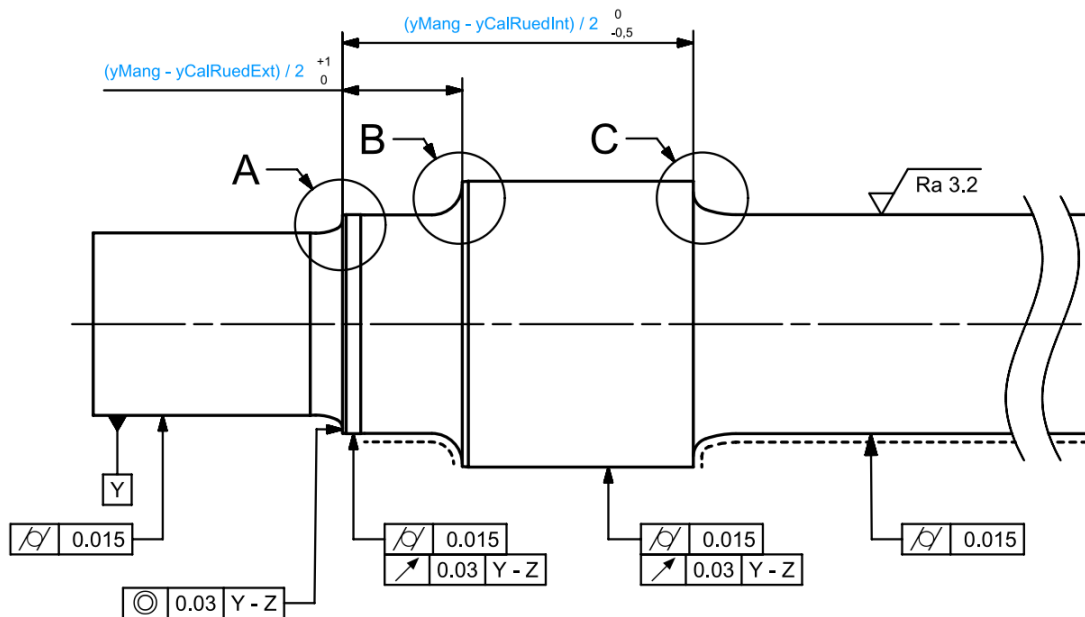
NX. Requerimientos planimetría asociados automáticamente a la geometría.
